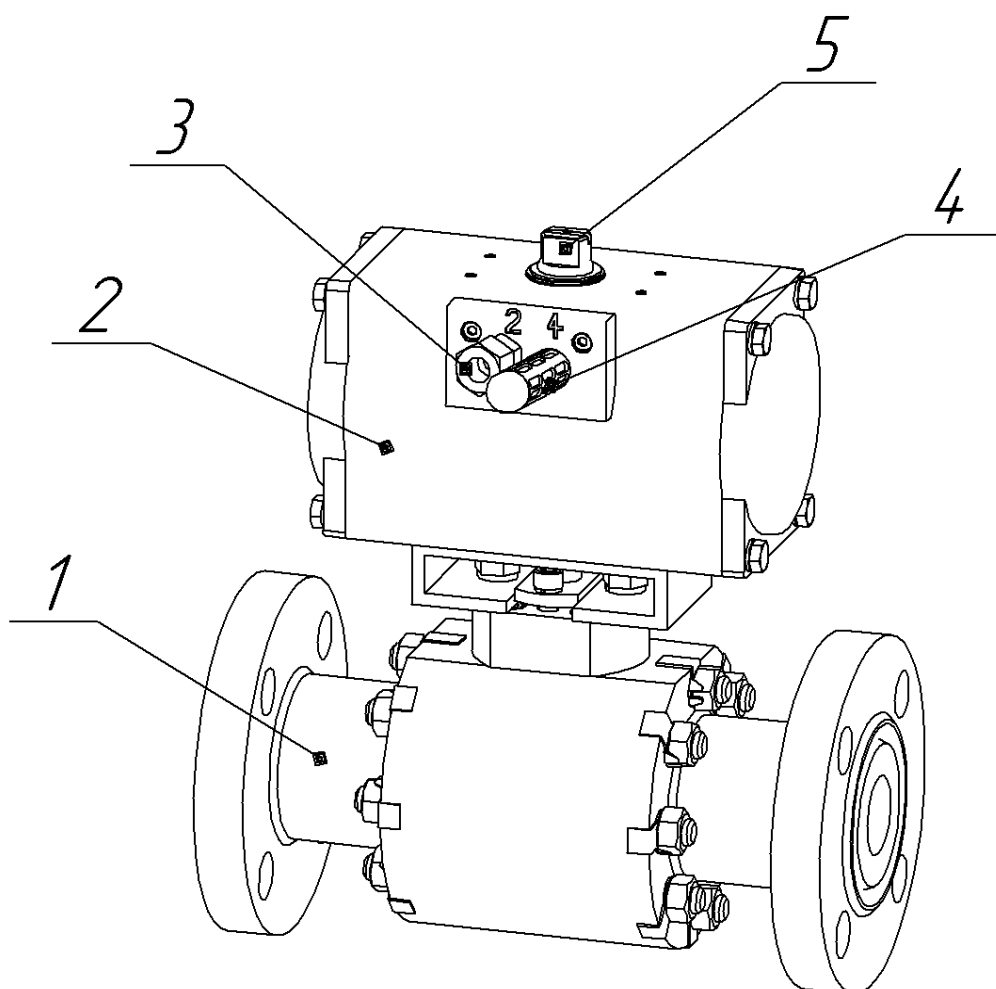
Габаритный чертеж устройства РУС-Ш с пусковым узлом
